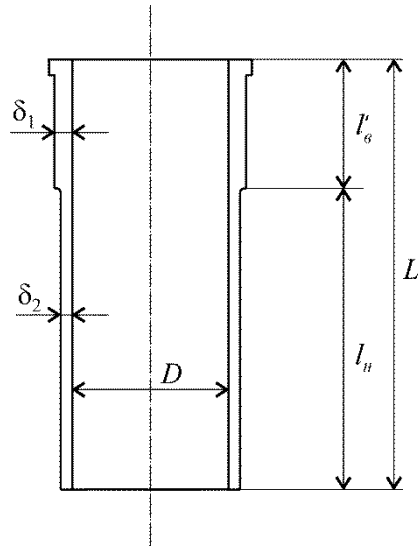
Эскиз цилиндровой втулки со ступенчатым изменением толщины вдоль её образующей
